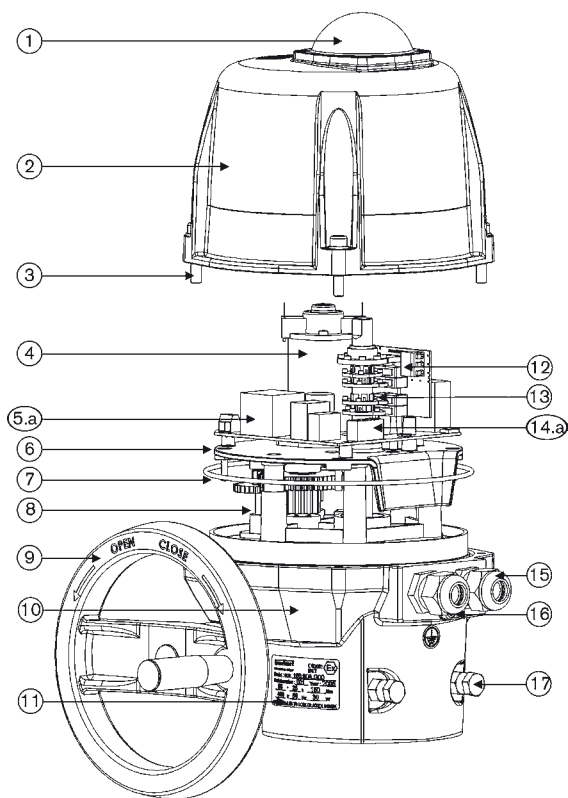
Vue éclatée du moteur 25 - 75 Nm
